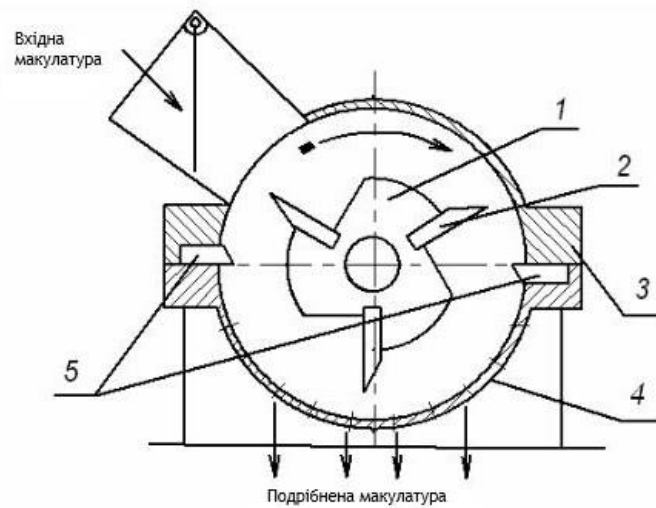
Схема принципу роботи подрібнювача ZS Voit: 1 – ротор ; 2 – ніж ротора ; 3 – корпус ; 4 – решітка ; 5 – ножі статора.
